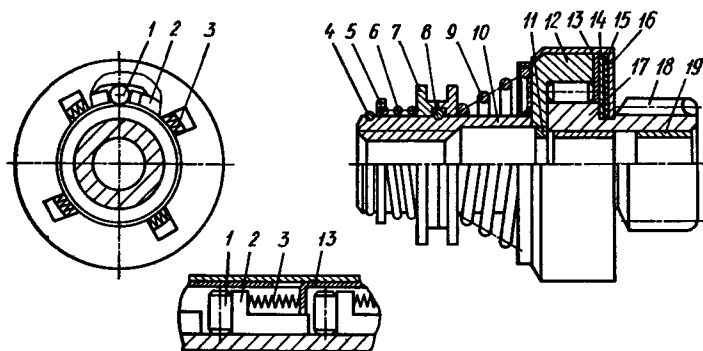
Привод стартера с бесплунжерной муфтой свободного хода:
